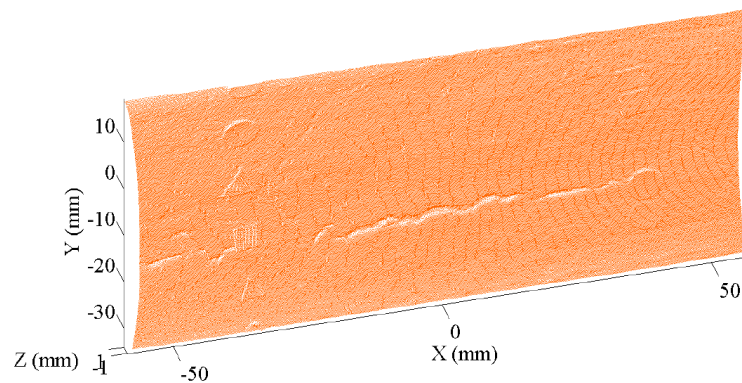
Reconstrucción 3D de la superficie con grieta en la capa externa
